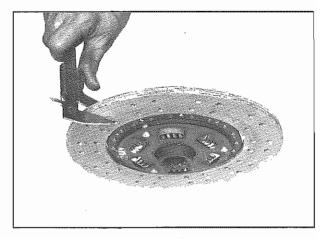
Controllo dell'usura del disco frizione Checking the clutch disc wear
